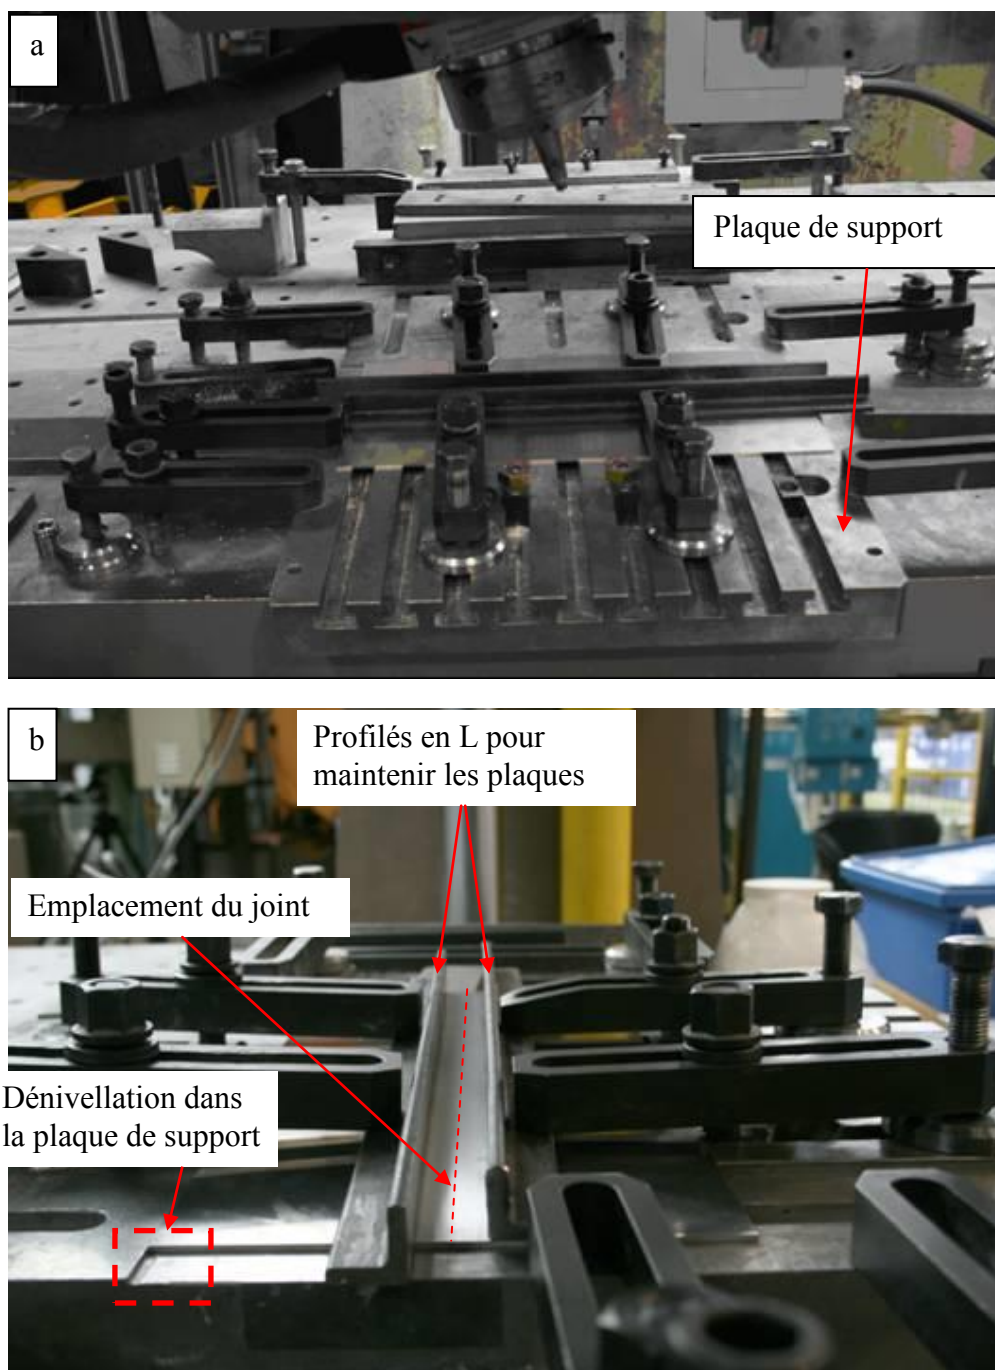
Photos du montage sur la machine MTS I-STIR PDS. (a) vue globale avec l'outil au-dessus du joint, (b) vue mettant en évidence les profilés et le joint au milieu avant le soudage.
